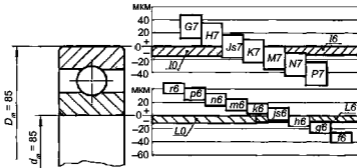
Схемы расположения рекомендуемых полей допусков посадочных размеров внутренних и наружных колец подшипника
